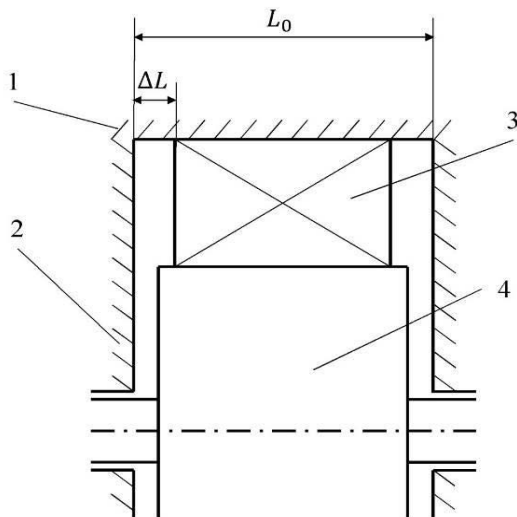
Поздовжній переріз пластинчато-роторного вакуумного насоса: 1 – статор; 2 – бокова кришка; 3 – лопатка; 4 – ротор
